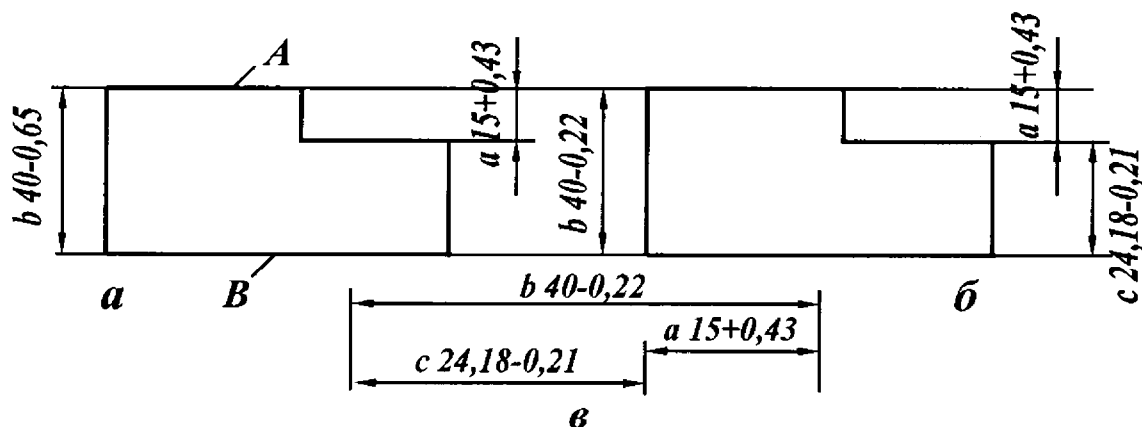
Чертеж детали (а) и эскиз обработки (б)
